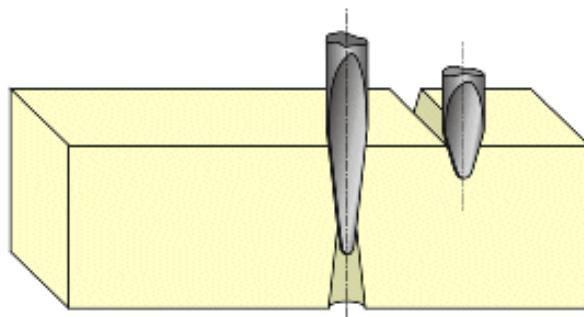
Изготовление рельефной заготовки методом фрезерования
